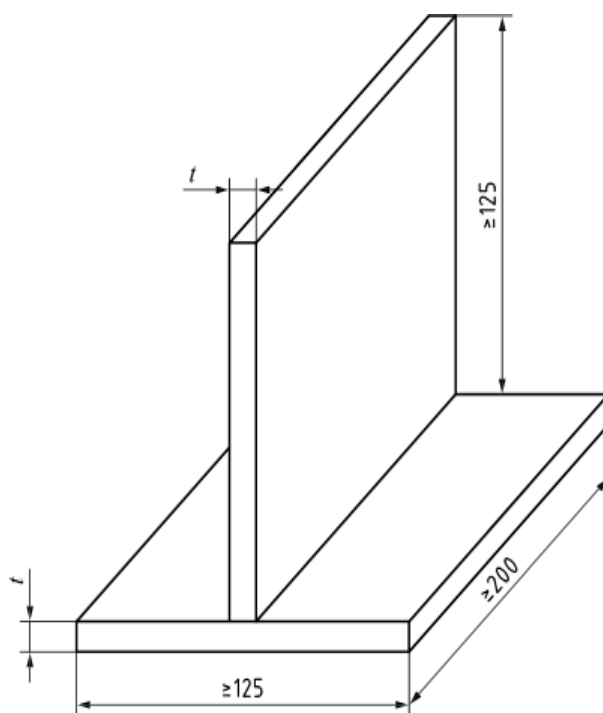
Розміри пластин для експертизи зварювання на кутових з'єднаннях.
